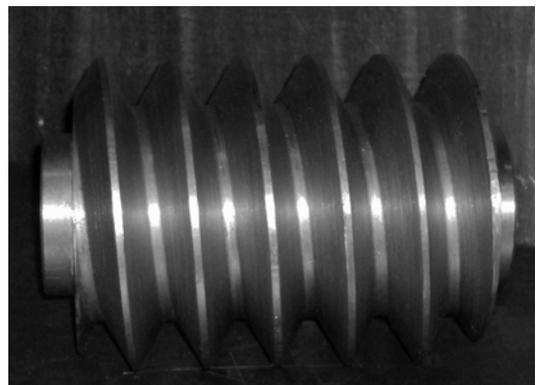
Корпус червячной фрезы с модулем 10 мм с обработанной винтовой поверхностью конволютного типа
